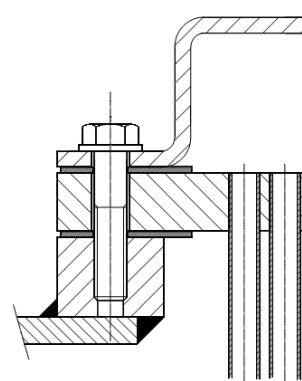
Disposición de montaje en la parte superior, pernos estándar.
